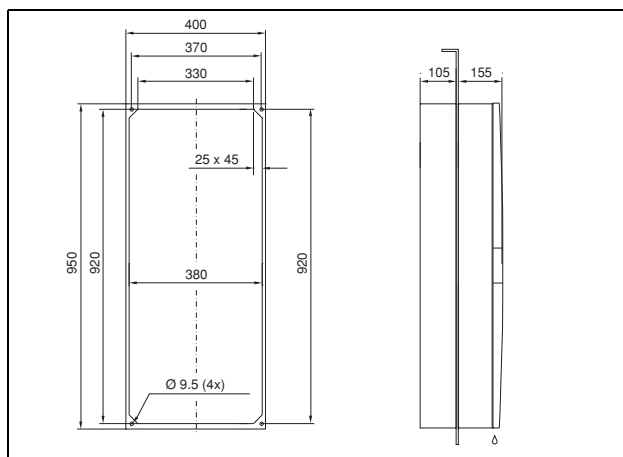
3304.xxx, 3305.xxx полутопленный монтаж
